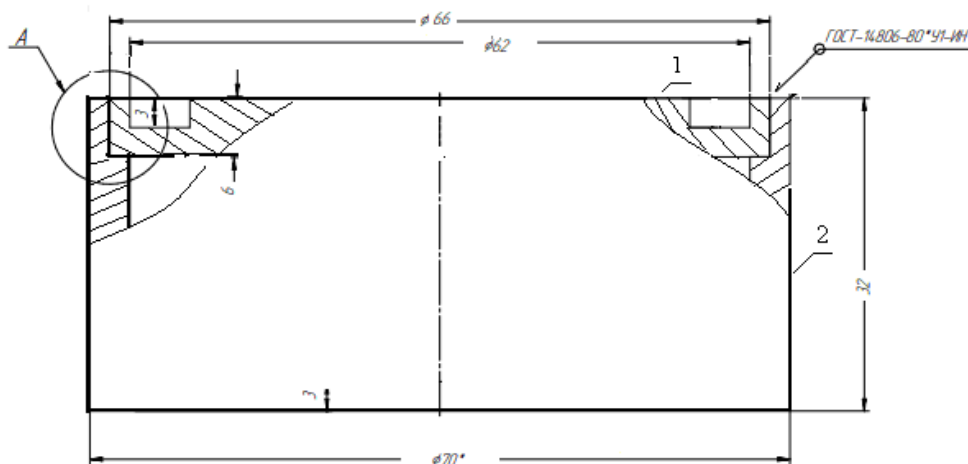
Схема подготовки кромок свариваемых деталей
